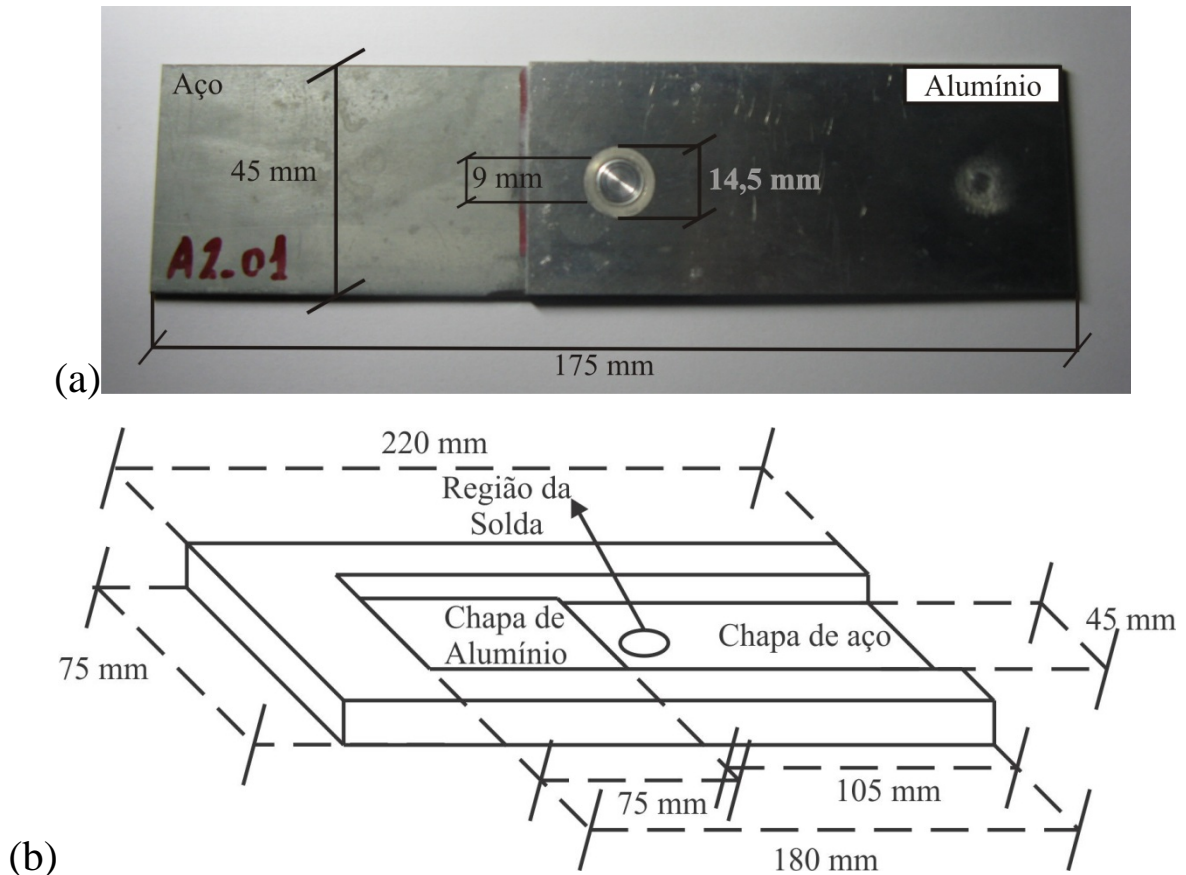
(a) Foto do corpo de prova soldado; (b) Dimensões do dispositivo desenvolvido para realizar as soldas nas dimensões requeridas pela Norma DIN EN ISO 1472:2002-03.
